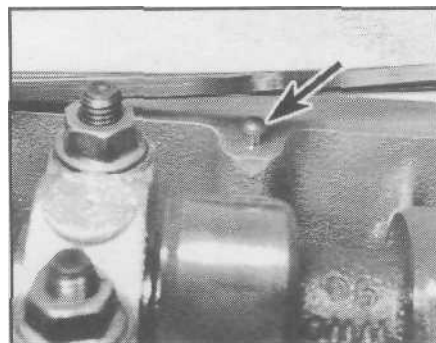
Установочный штифт для прокладки крышки головки цилиндров (показан стрелкой)
